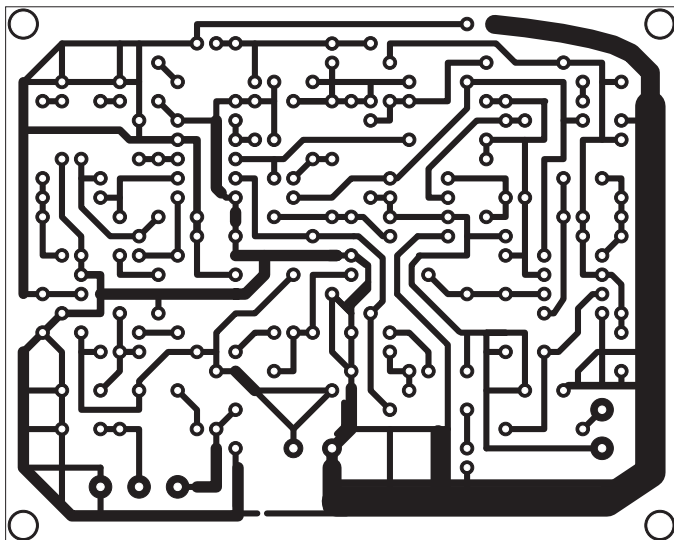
Layout der einseitigen Platine des Drucksensors; Abmessungen 89 mm x 71,1 mm, M 1:1
